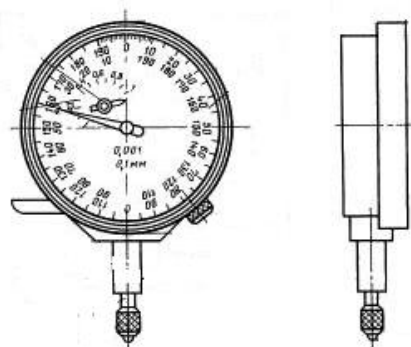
Ескіз індикатора багатооборотного моделі 2МИГ-1
